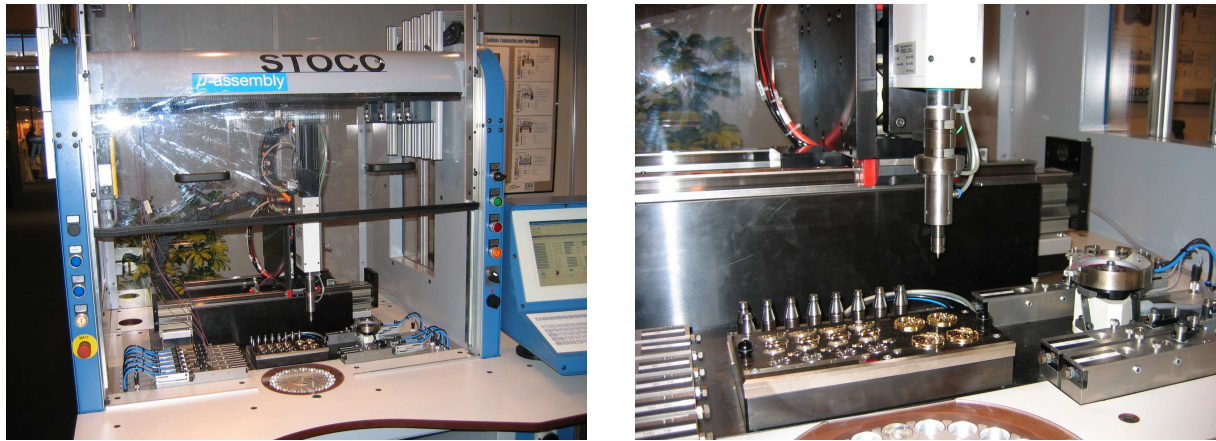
Prototype de la machine d'empierreage Stoco.
